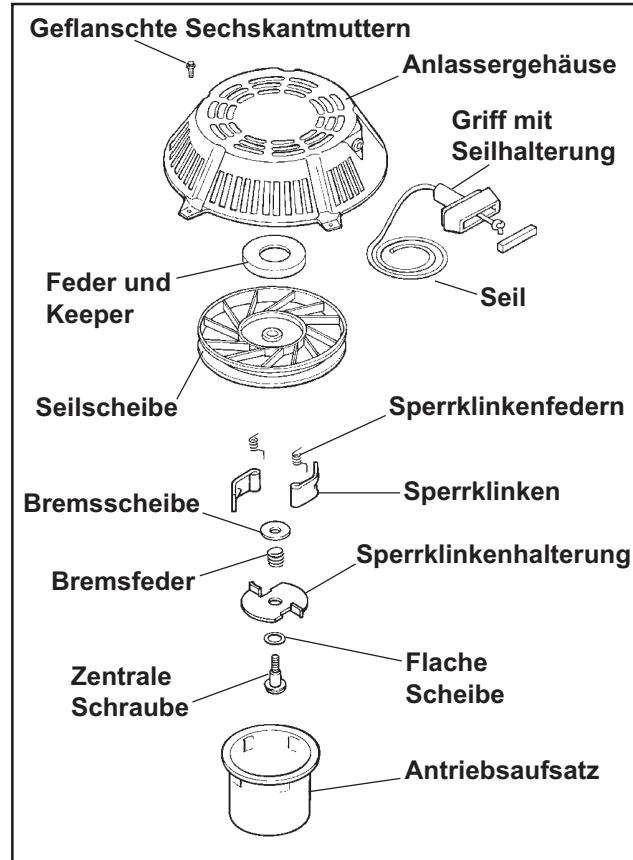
Seilzuganlasser - Explosionsansicht.
